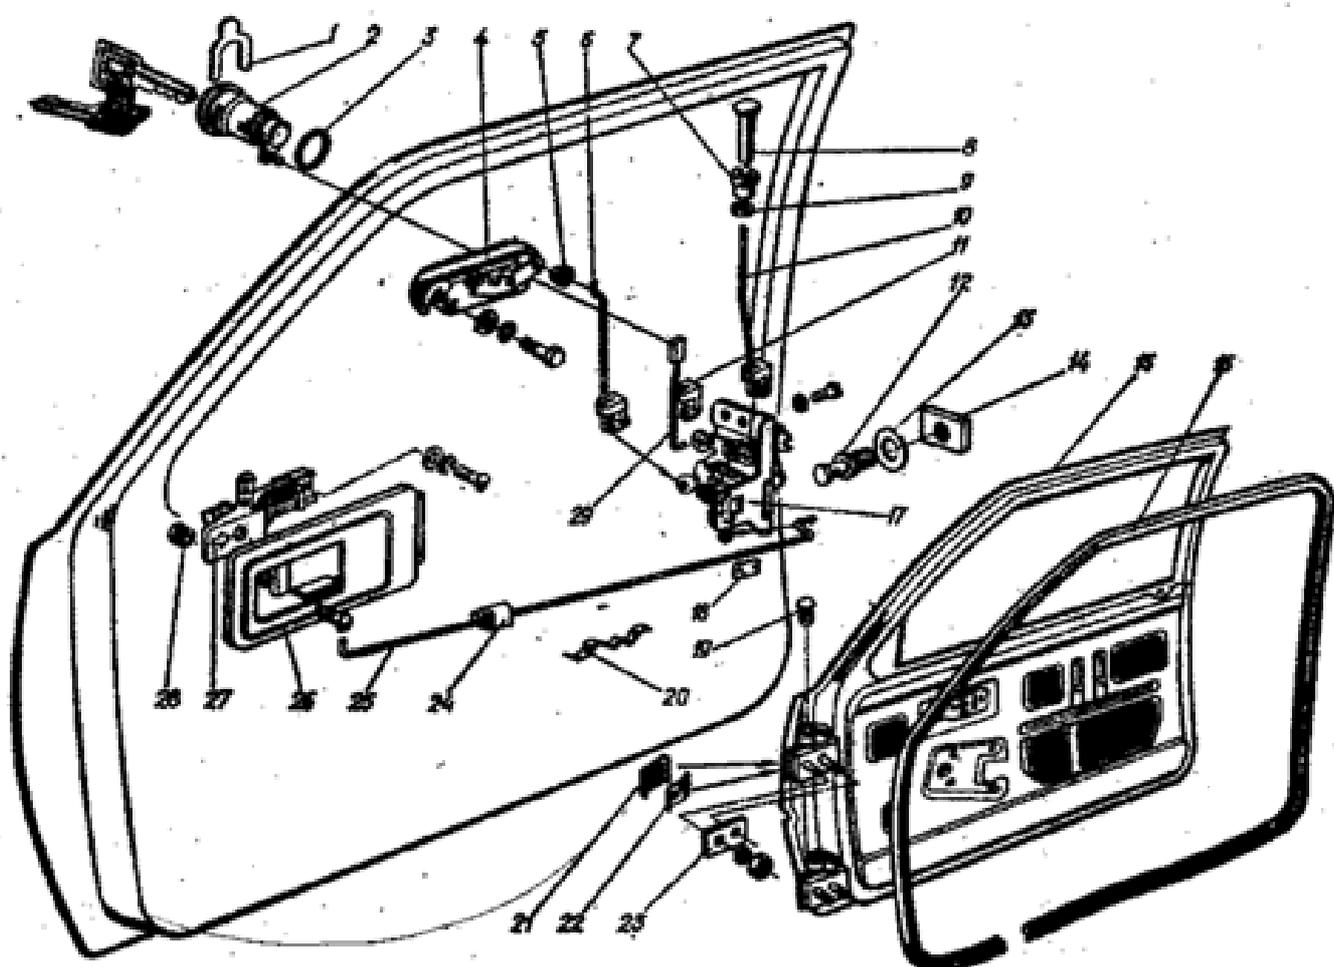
Дверь боковая и арматура двери (без стеклоподъемника) трехдверного автомобиля: 1 - скоба крепления выключателя; 2 - выключатель замка; 3 - уплотнитель; 4 - ручка двери наружная; 5 - втулка; 6 - тяга наружной ручки; 7 - розетка; 8 - кнопка; 9 - шайба розетки; 10 - тяга кнопки; 11 - скоба крепления тяги; 12 - фиксатор; 13 - шайба; 14 - пластина крепления фиксатора; 15 - дверь правая; 16 - уплотнитель двери; 17 - замок правой двери; 18 - прокладка; 19 - заглушка; 20, 21 - фиксатор; 22 - пружина; 23 - пластина крепления петли; 24 - держатель; 25 - тяга привода внутренней ручки; 26 - облицовка; 27 - ручка внутренняя; 28 - гайка специальная; 29 - тяга выключателя замка.
